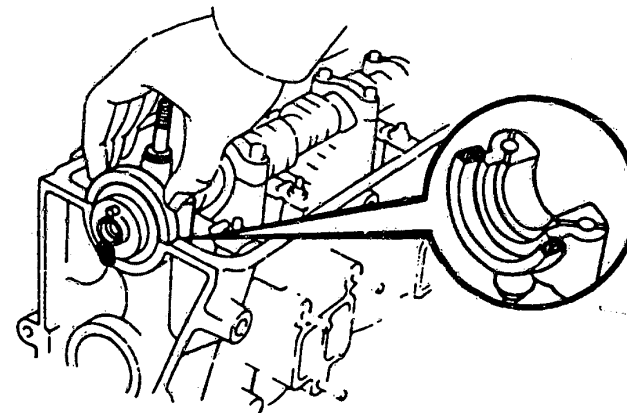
Am vordersten Lagerdeckel der Nockenwelle ist vor dem Einbau an den schraffierten Flächen Dichtungsmasse aufzutragen.
